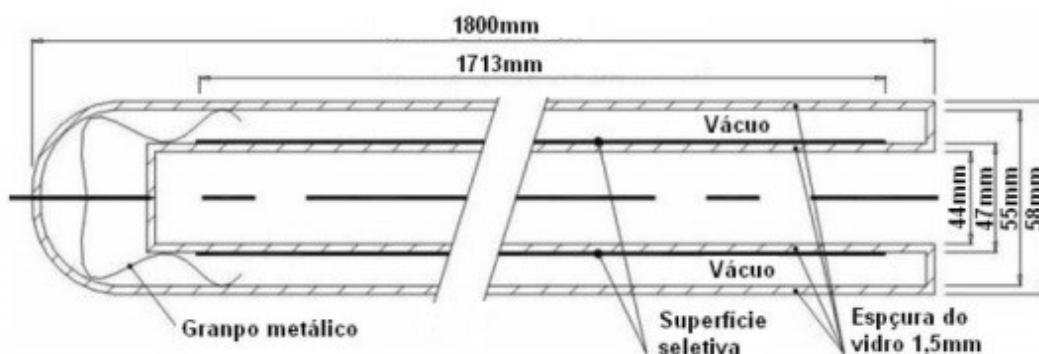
Dimensões de tubo comercial de coletor solar evacuado Fonte: Manea, 2012.
